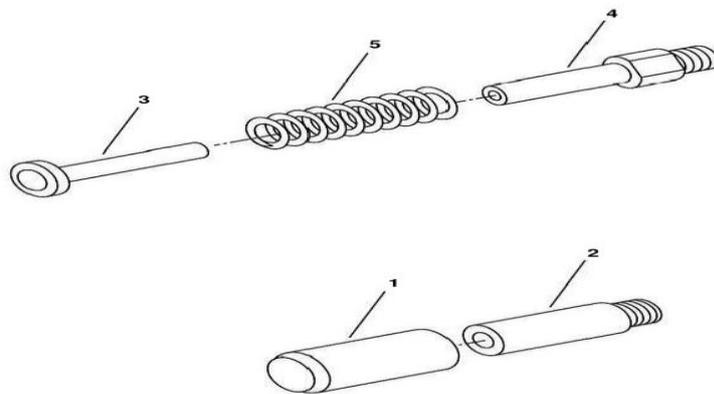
Componentes del pistón de control de las bombas de pistones Rexroth A10vO series 31. [16]
